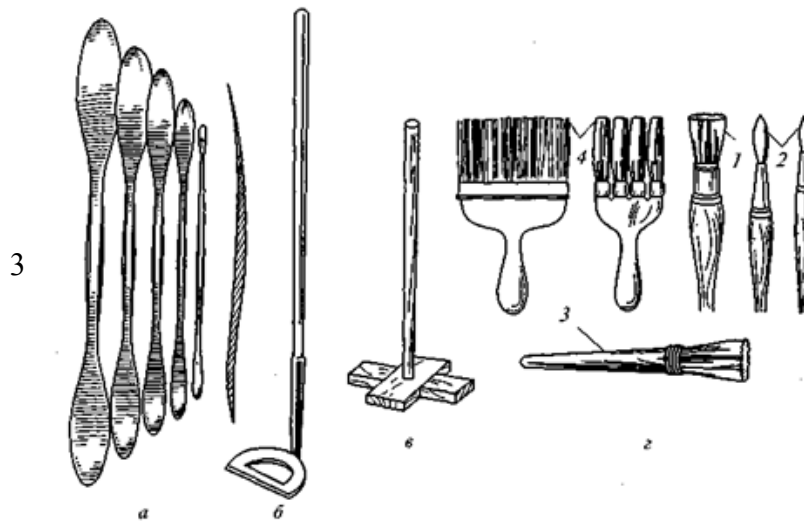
Вспомогательный инструмент: а — лопатки; б — мешалка; в — мутовка; г — кисти; 1 — проколотки; 2 — заправные; 3 — клеевые; 4 — флейцы
